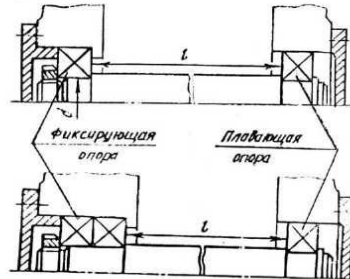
Схема осевого фиксирования вала в опоре с двумя одинарными или одним двойным подшипником
